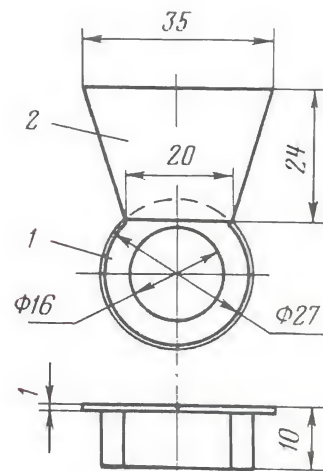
Вторая деталь: 1 — крышка; 2 — пластина.
